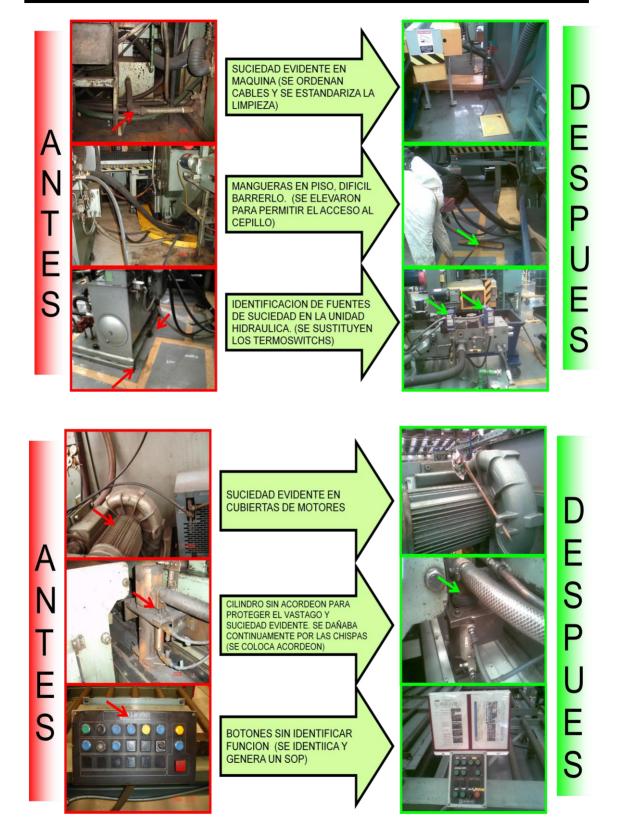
Lista de Limpieza Inicial Fuente: CNH Componentes
